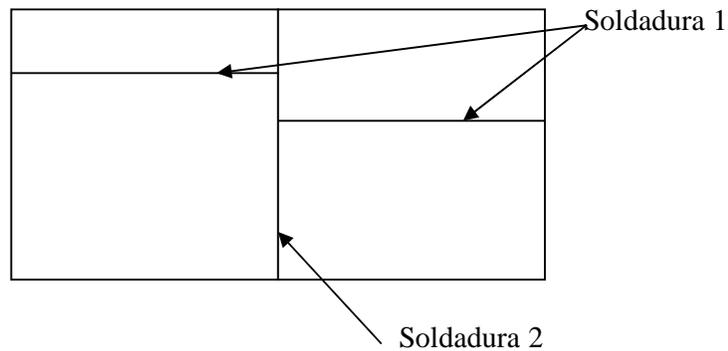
Categoría de juntas soldadas en el cuerpo
